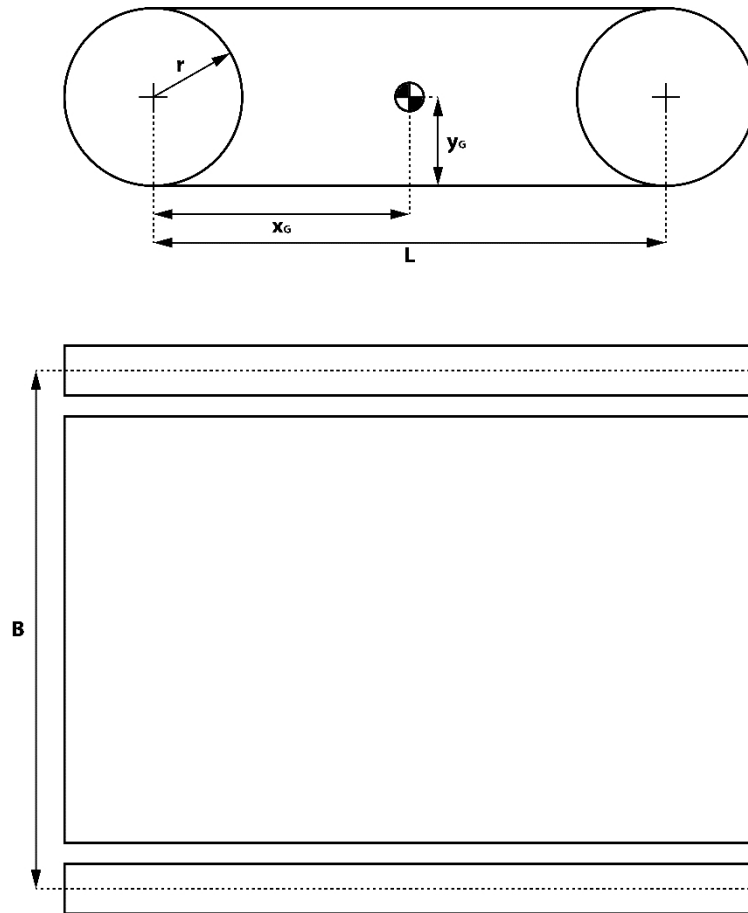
Dimensiones relevantes de un escalador de gradas de geometría fija.
